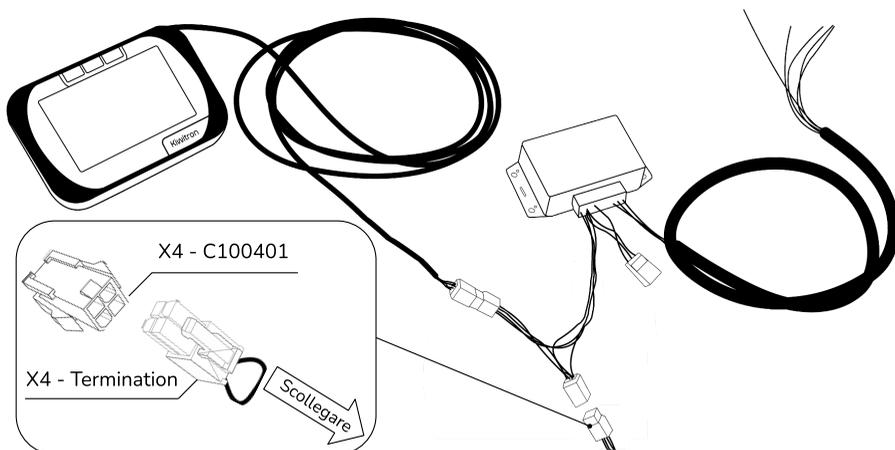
Scollegamento terminazione X4 (chiusura CAN)
